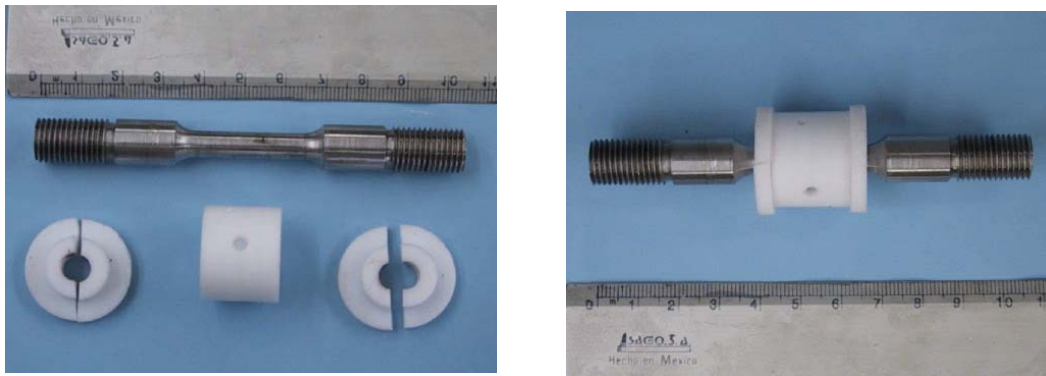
Detalle del ensamblaje de la “camara aislante” utilizada en el segundo arreglo
